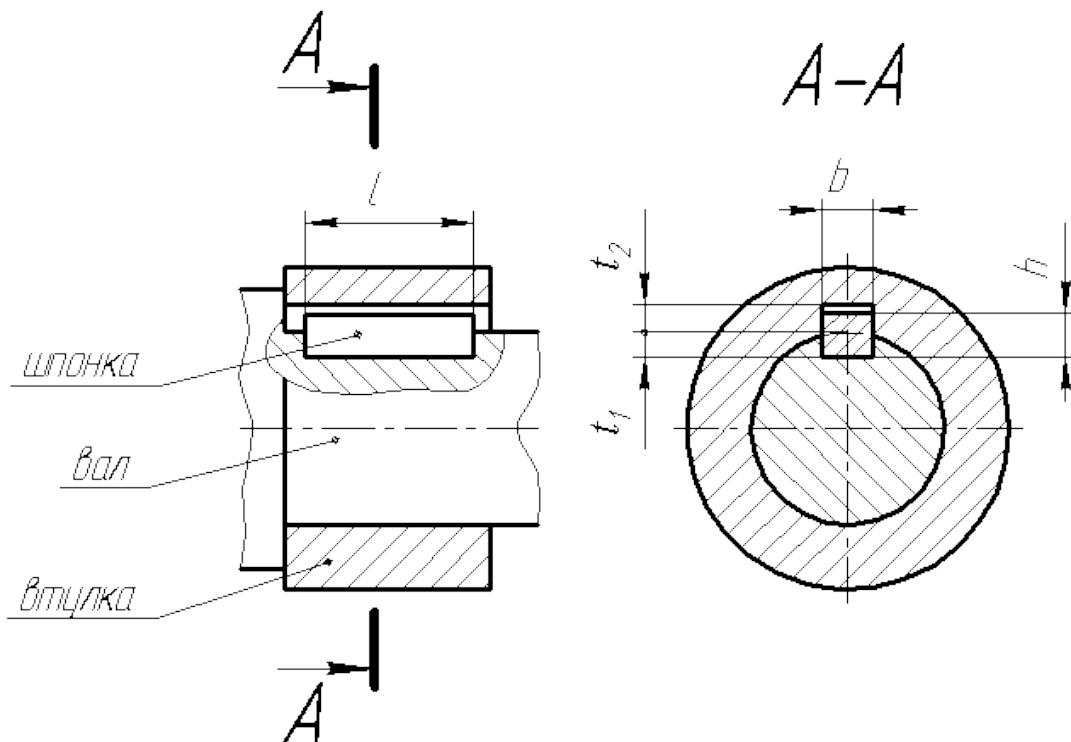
Розрахункова схема шпонкового з'єднання
